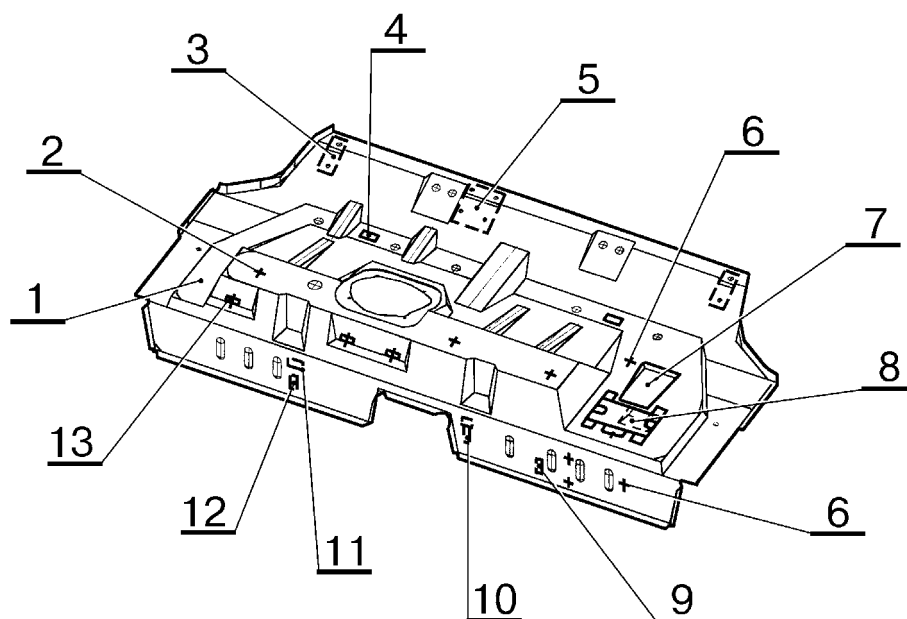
Детали панели пола 1118-5101032 средней в сборе. Номера и наименования деталей, количество сварочных точек приведены в таблице 9.
